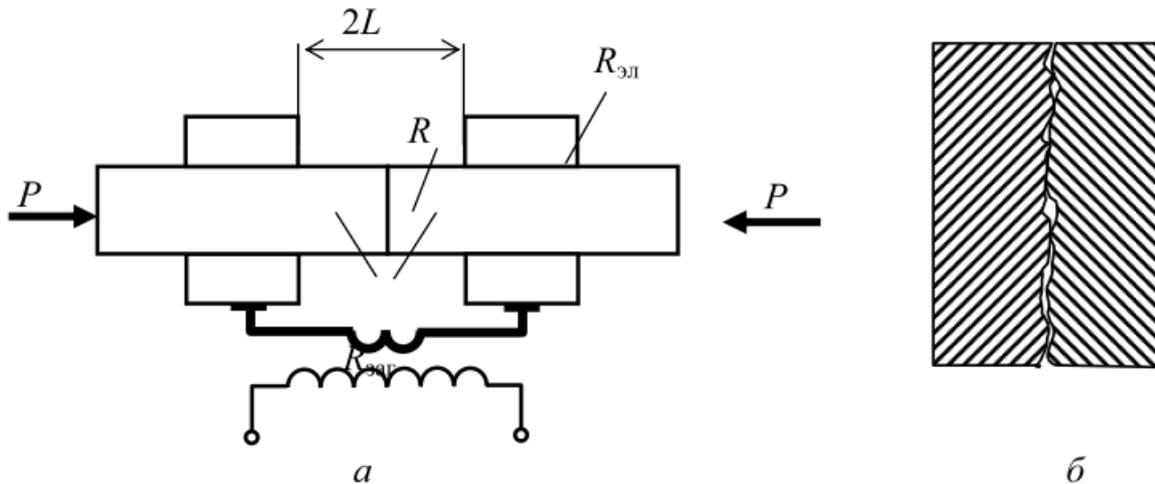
Стыковая электроконтактная сварка сопротивлением:
